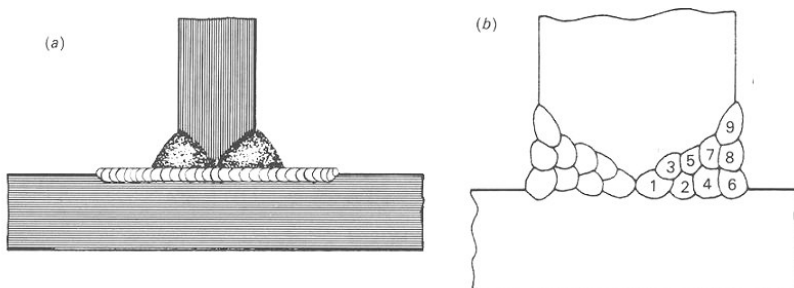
Princípios de (a) almofadamento e (b) almofadamento durante a própria soldagem para reduzir o risco de decoção lamelar
